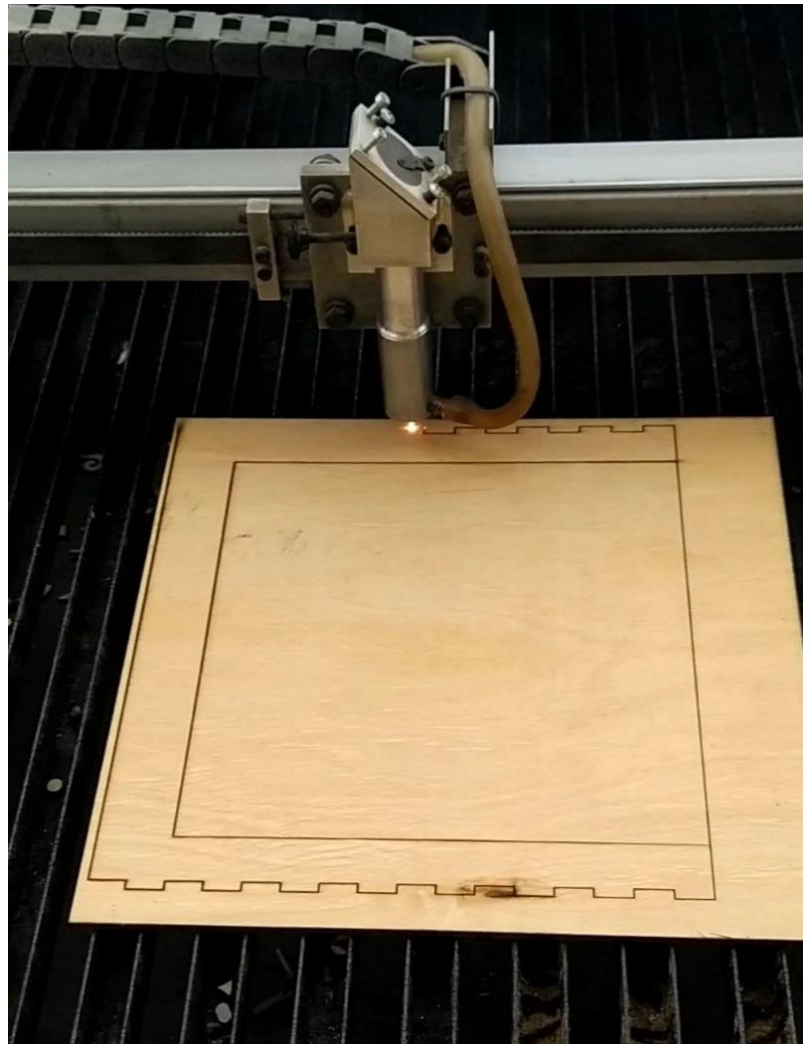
Процес виготовлення макета на лазерному верстаті
